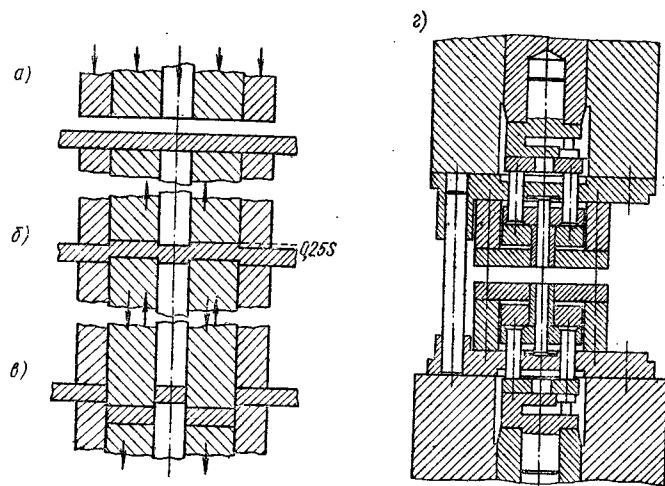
Реверсивный способ чистовой вырубке и штампы для нее
